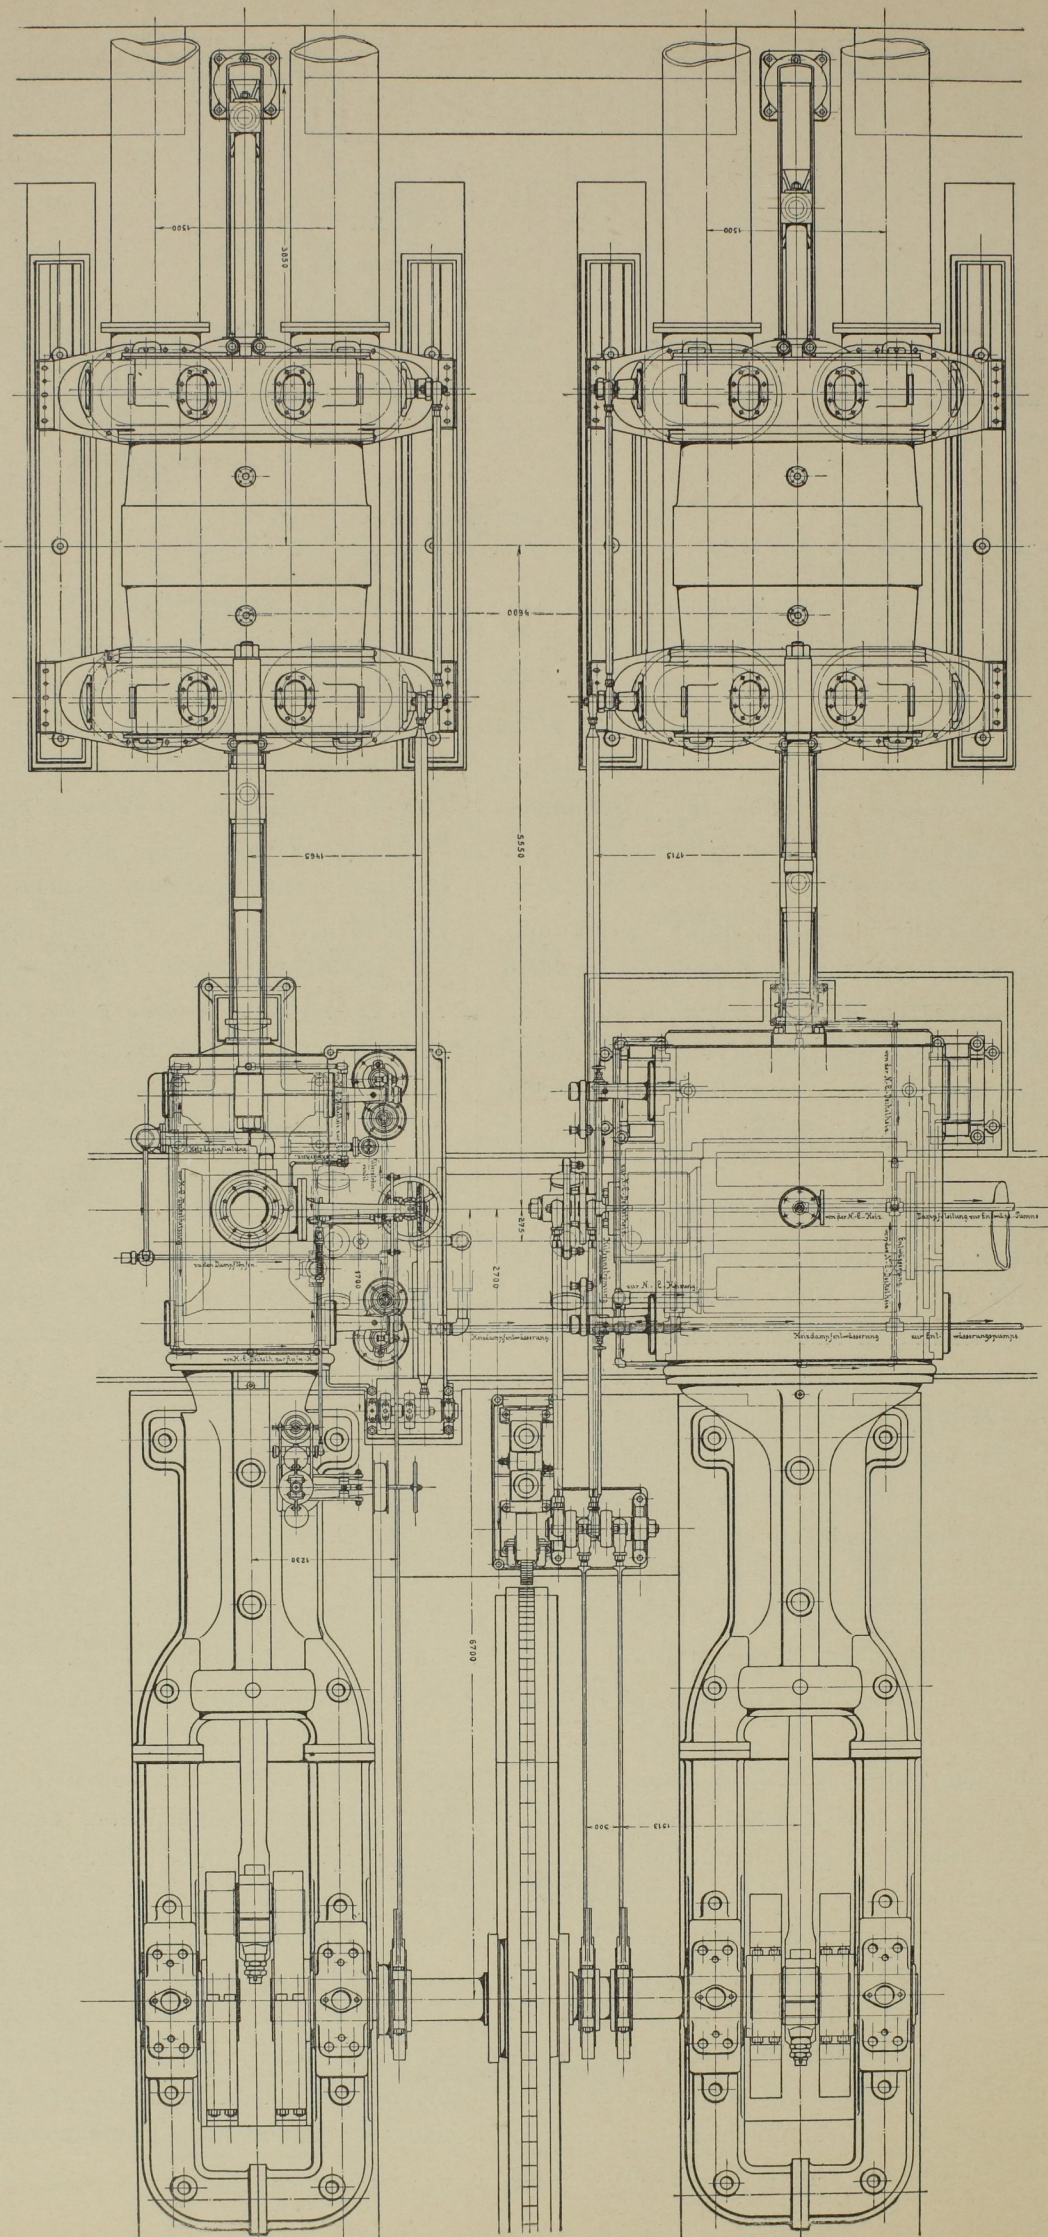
Grundriss der Gesamtanordnung. Massst. 1 : 60.
